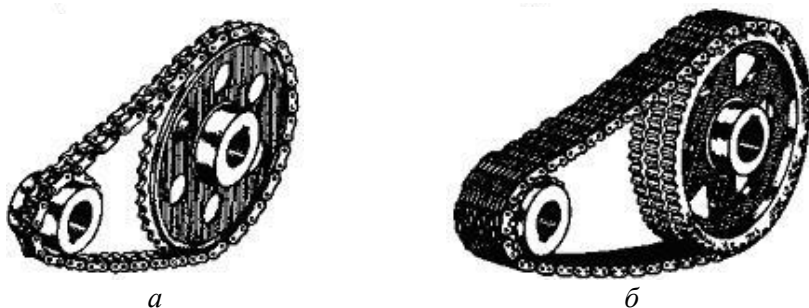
Цепная передача роликовой (а) и зубчатой (б) цепью
